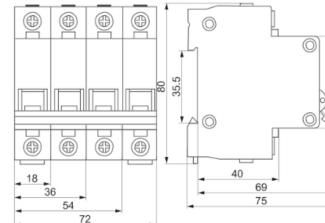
Габаритные, установочные, присоединительные размеры выключателей
